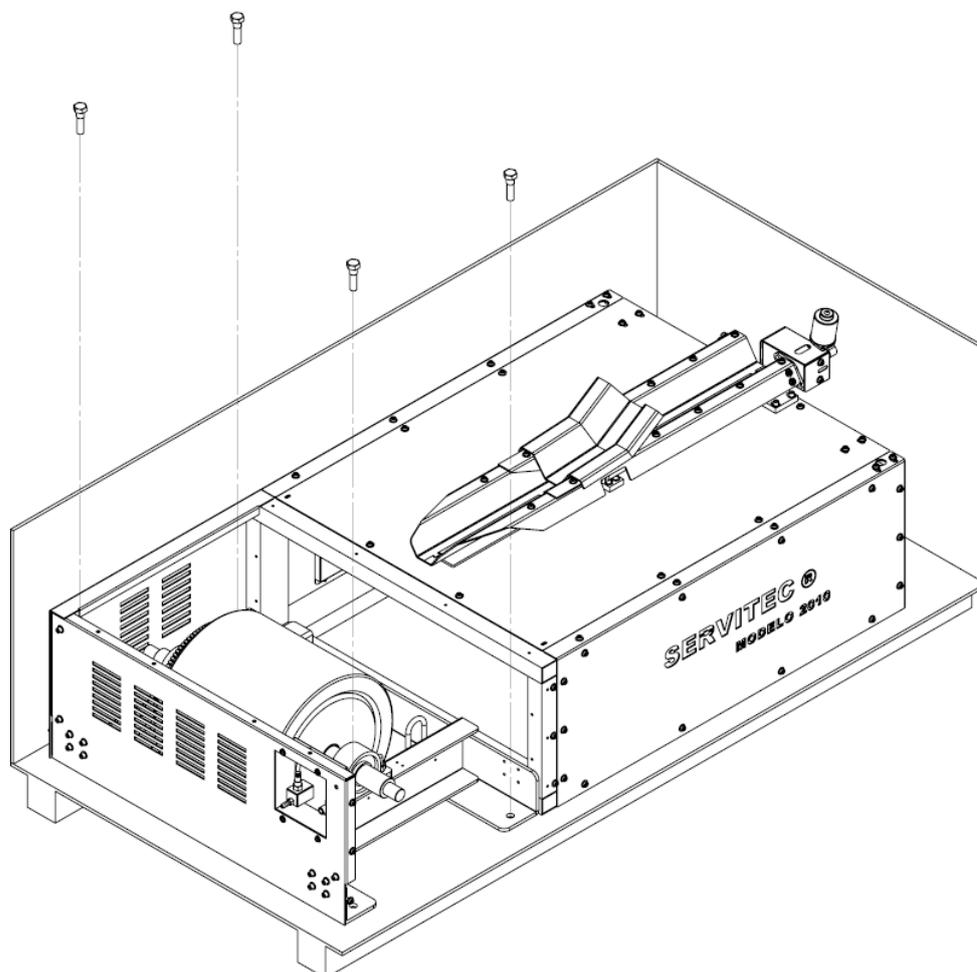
Remoção dos parafusos de fixação da tampa do Rolo
